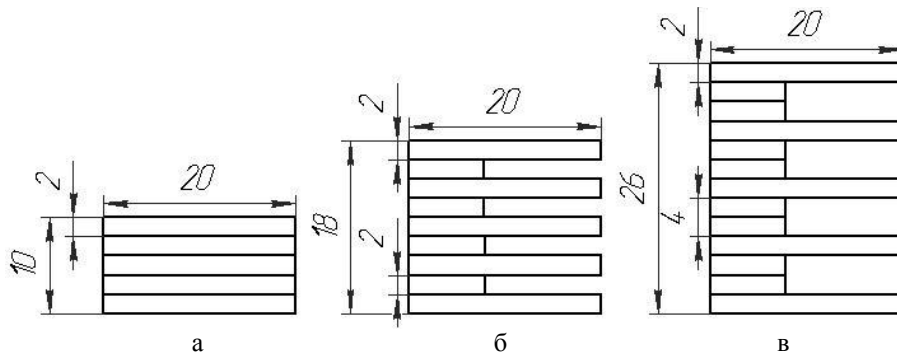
Размеры и конструктивные особенности обрабатываемого пакета
